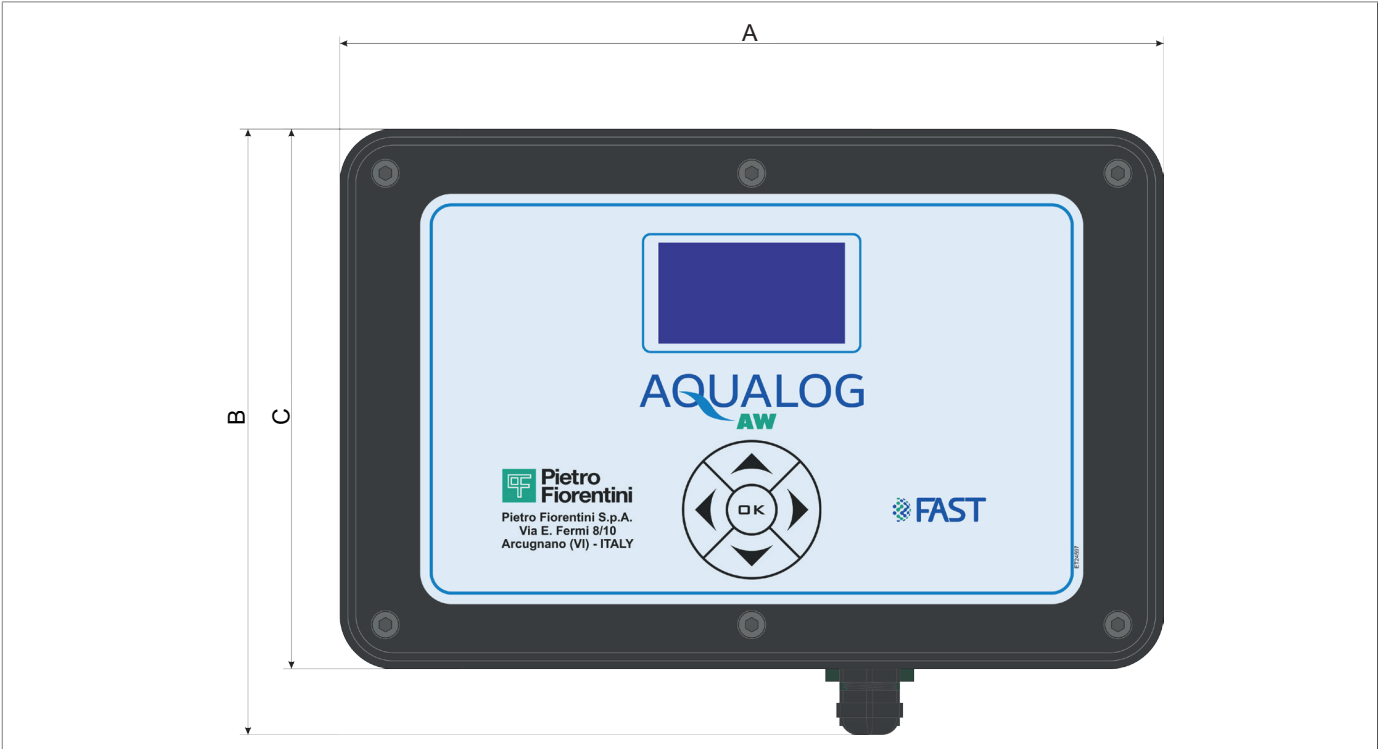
Dimensiones AQUALOG AW Versión con conector MIL, vista frontal
